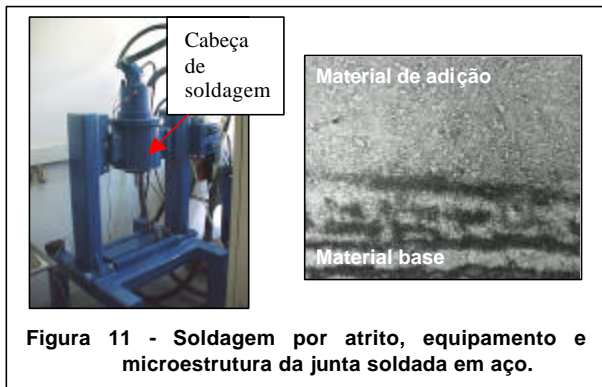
Soldagem por atrito, equipamento e microestrutura da junta soldada em aço.
